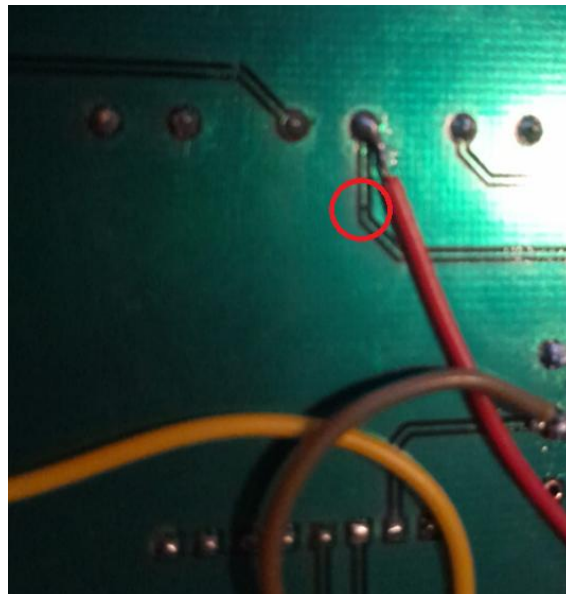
Defecto de ruta discontinua en PCB del EPS.
